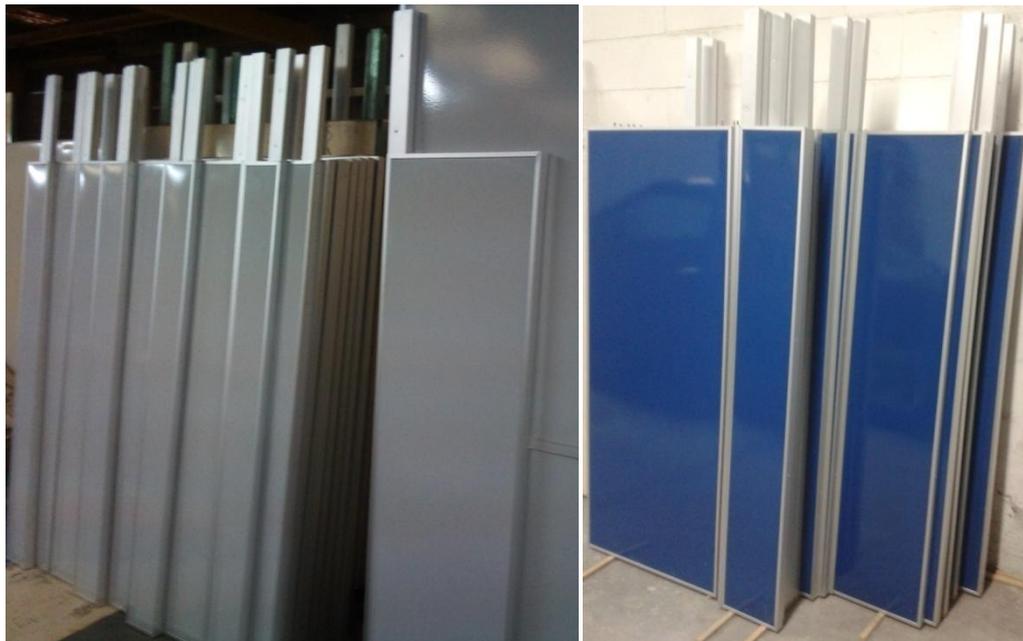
CONJUNTO DE PIEZAS YA TERMINADAS, LISTAS PARA SER ENTREGADAS E INSTALADAS
